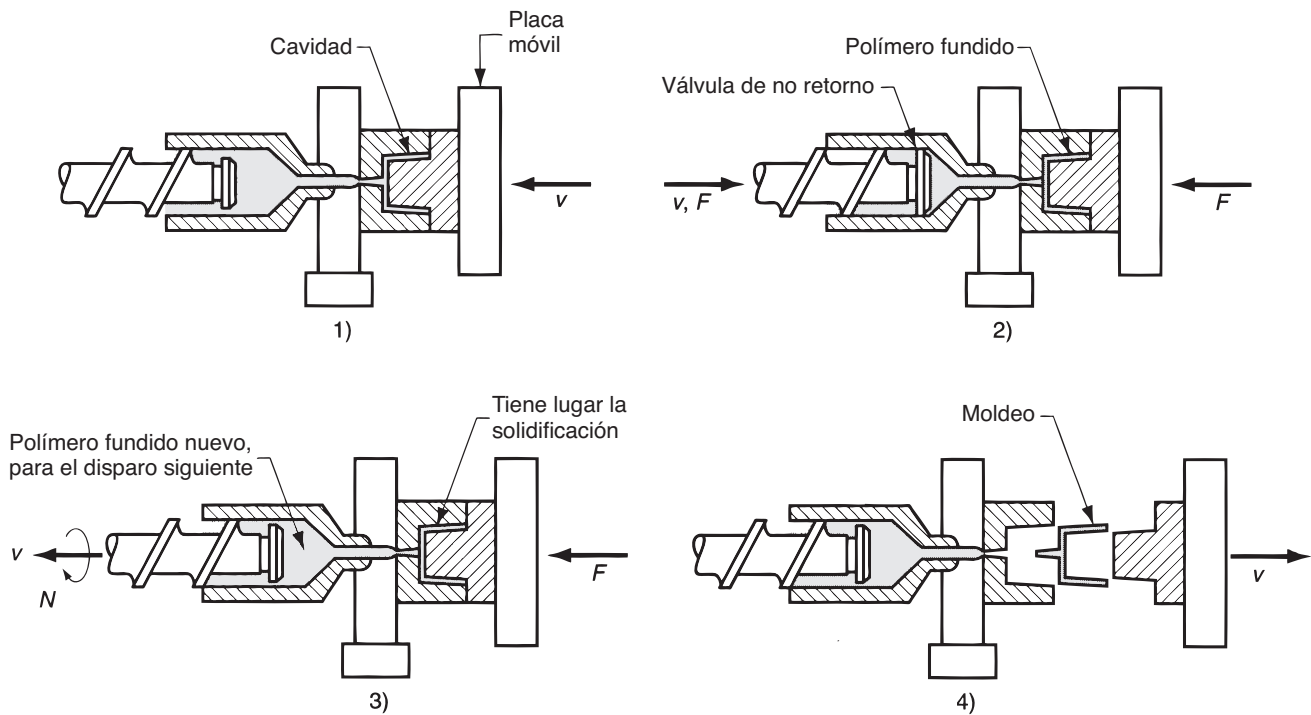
Ciclo común de moldeo: 1) molde cerrado, 2) se inyecta fluido a la cavidad, 3) se retrae el tornillo y 4) se abre el molde, y la pieza se expulsa.
